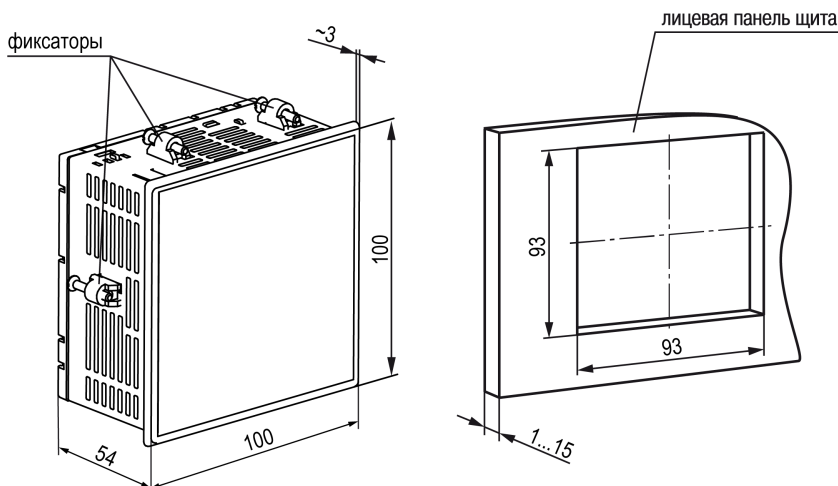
Габаритные размеры корпуса и монтажного отверстия в щите
